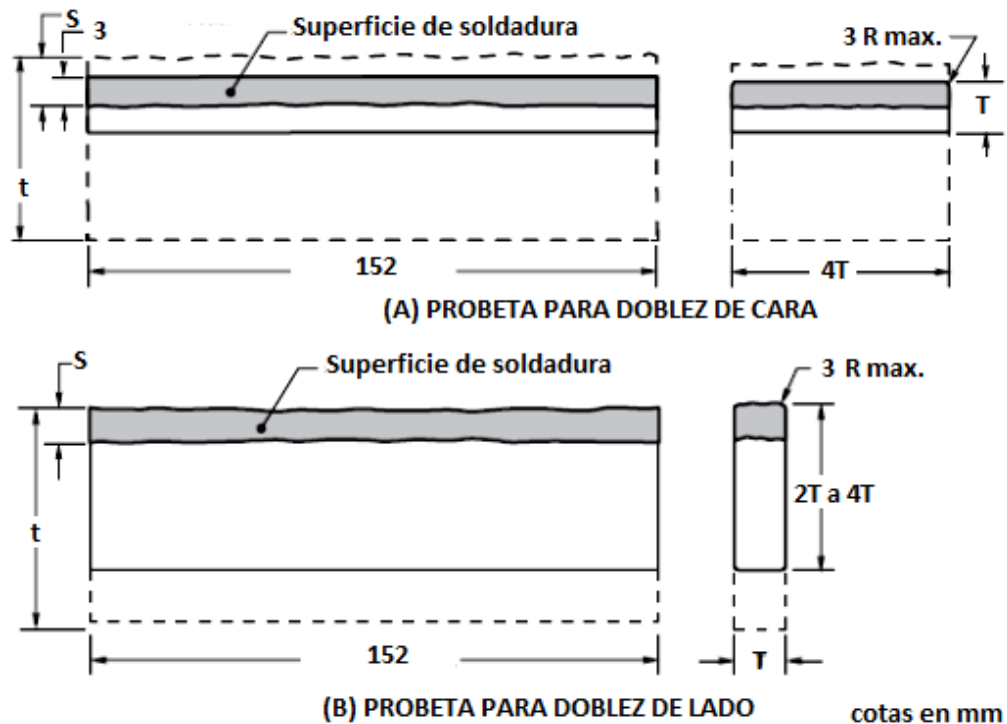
Probetas de soldadura de superficies [3].
